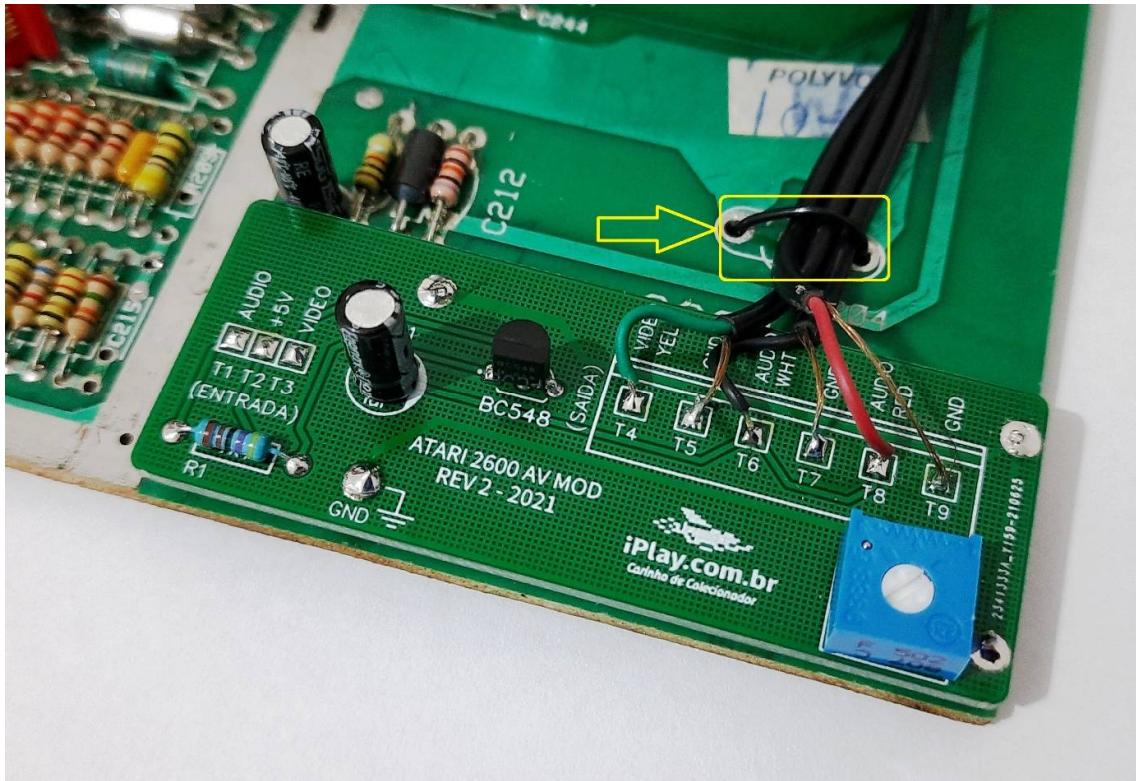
Cabo AV Soldado na Placa AV
